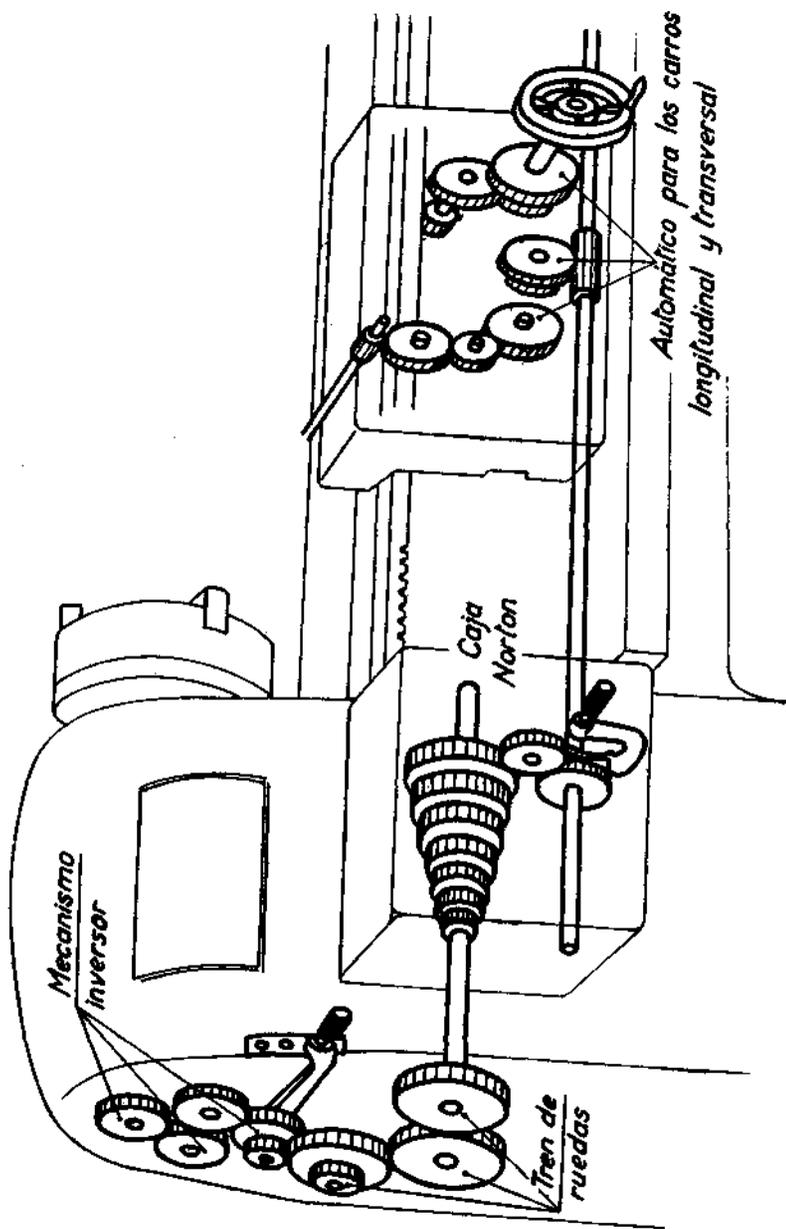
Esquema del sistema de engranajes para el avance automático del carro longitudinal y del carro transversal
